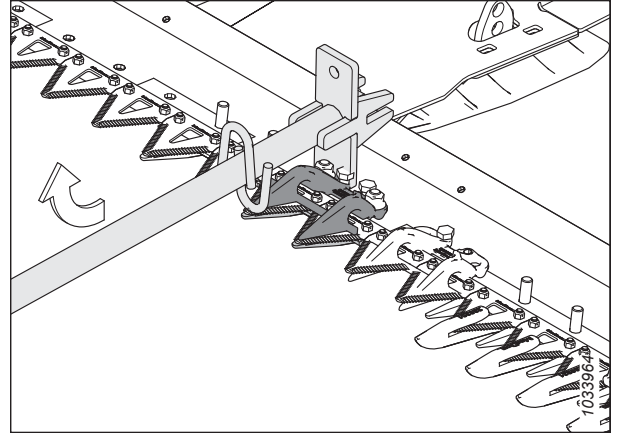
Регулировка смещением вверх — укороченный противорежущий палец
